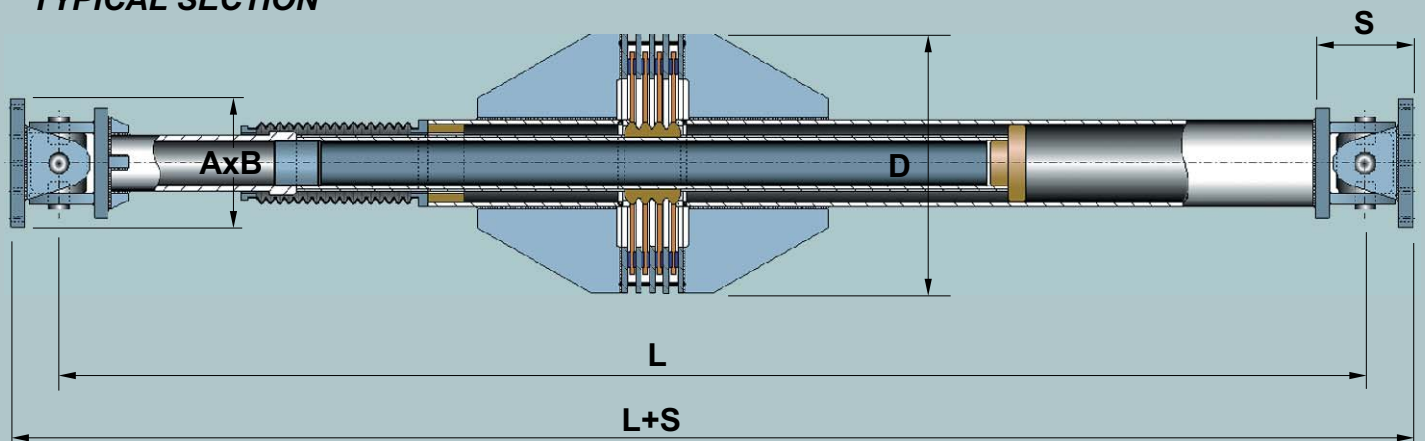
ALGASISM DECS rotativo passivo - Rotating passive ALGASISM DECS
